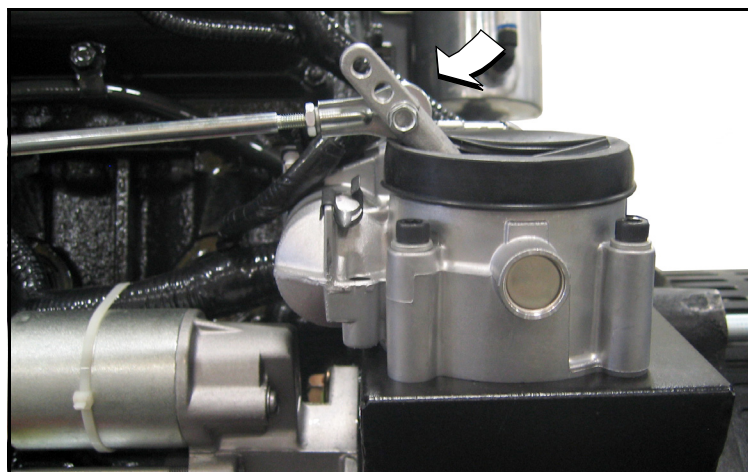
Lubrification des extrémités de la tige du régulateur
